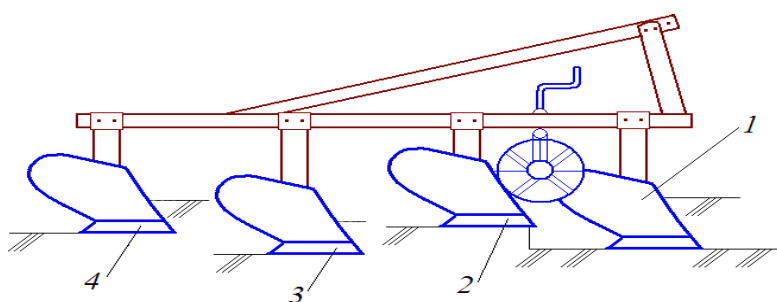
Четырехкорпусный плуг для ступенчатой вспашки
